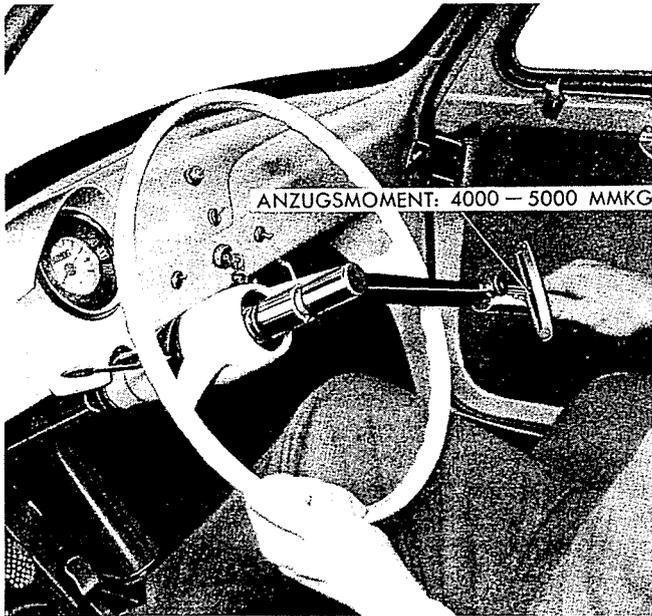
Anziehen der Befestigungsmutter des Lenkrads.
